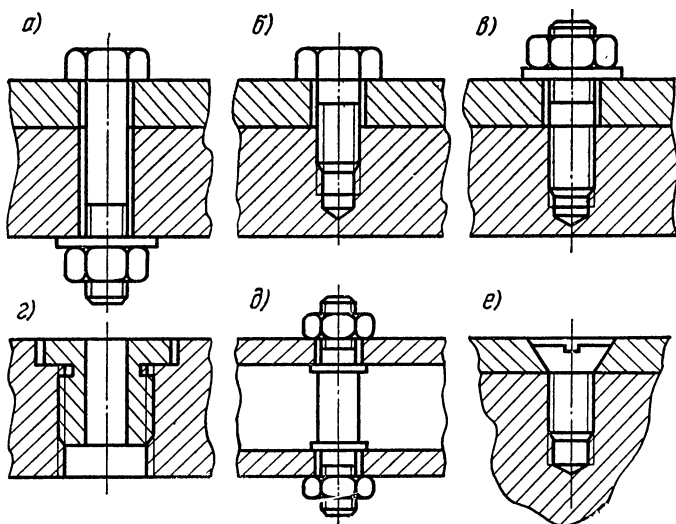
Резьбовые соединения при сборке: а — болтовое; б, в — винтовое; в — шпильчное; г — резьбовой втулкой; д — распорное
